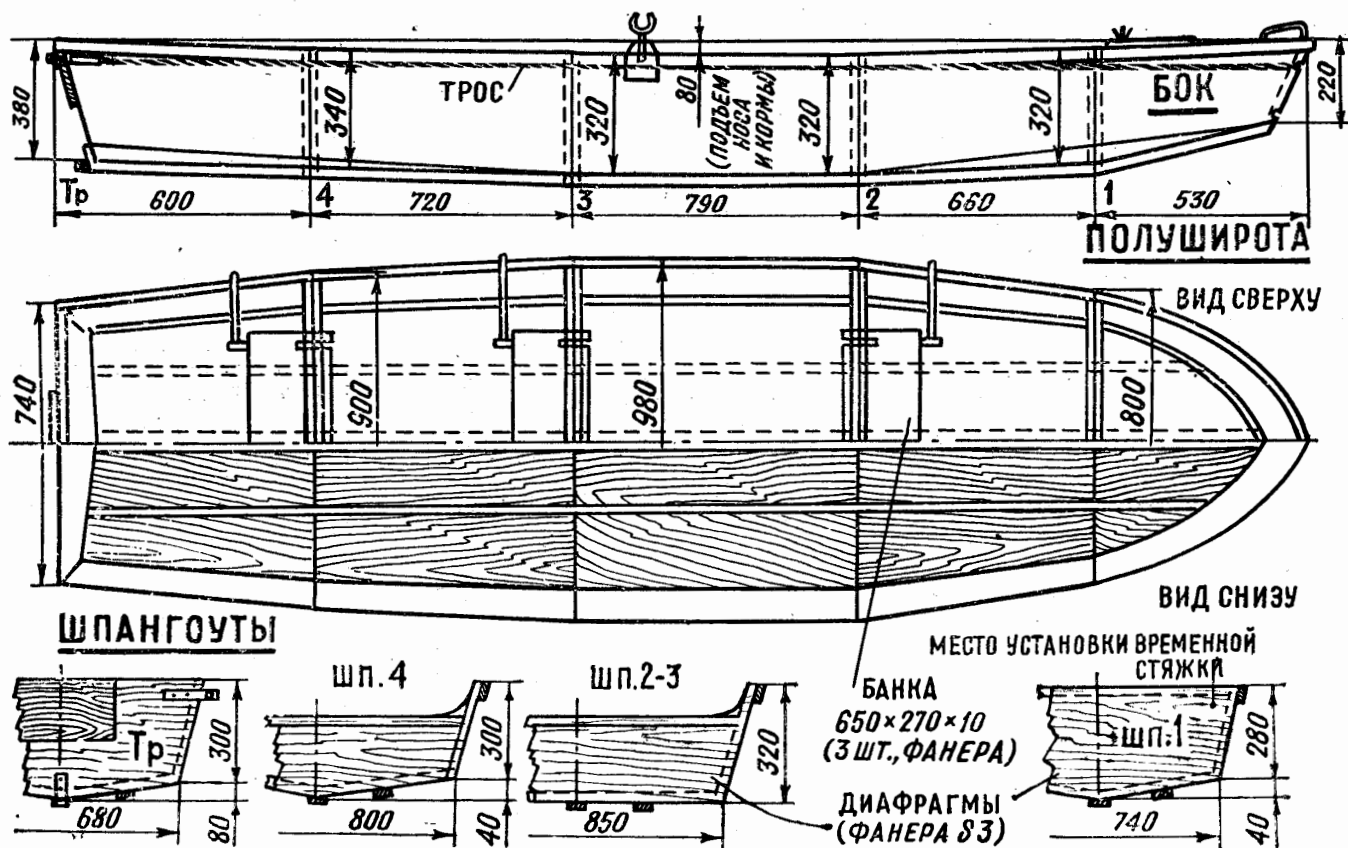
Основные размеры лодки «Краб», конструкция корпуса и шпангоутов.
